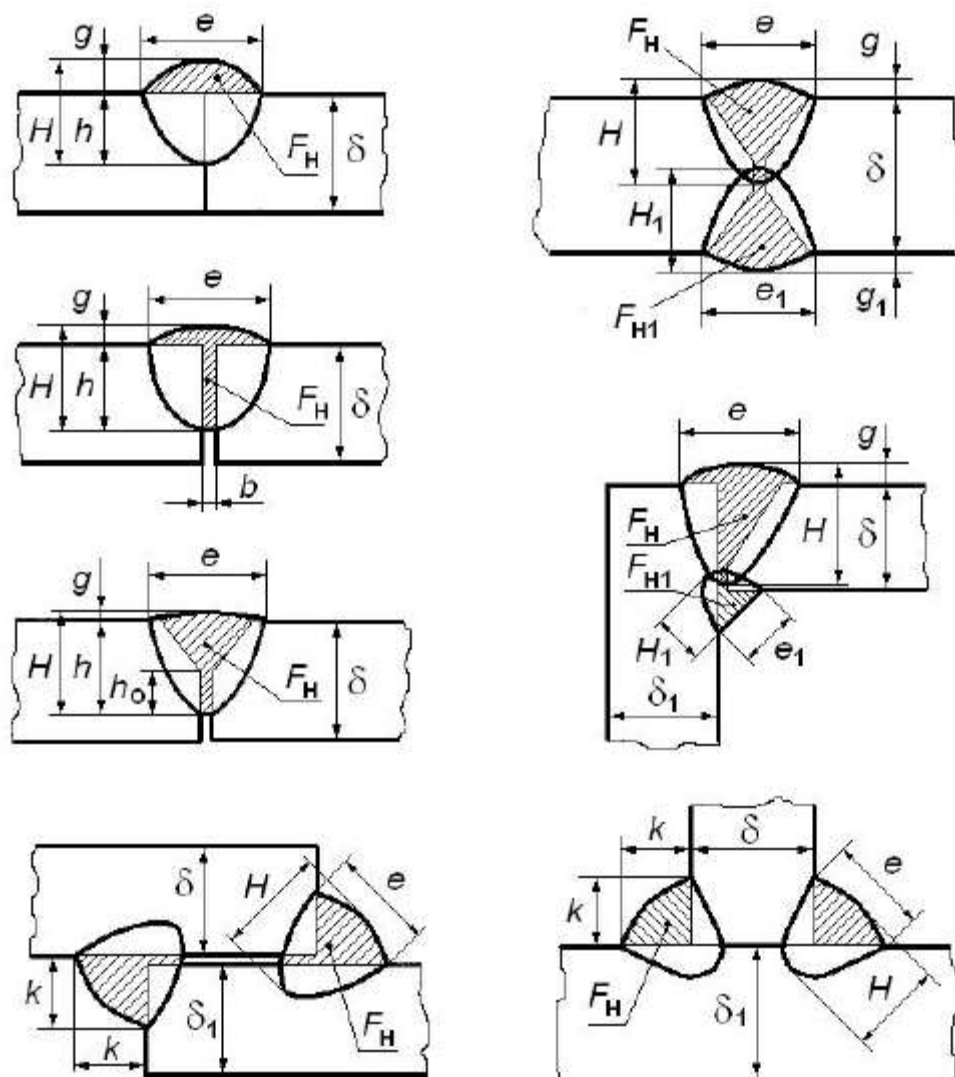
Исходные геометрические размеры сварных швов при расчете основных параметров режима сварки
